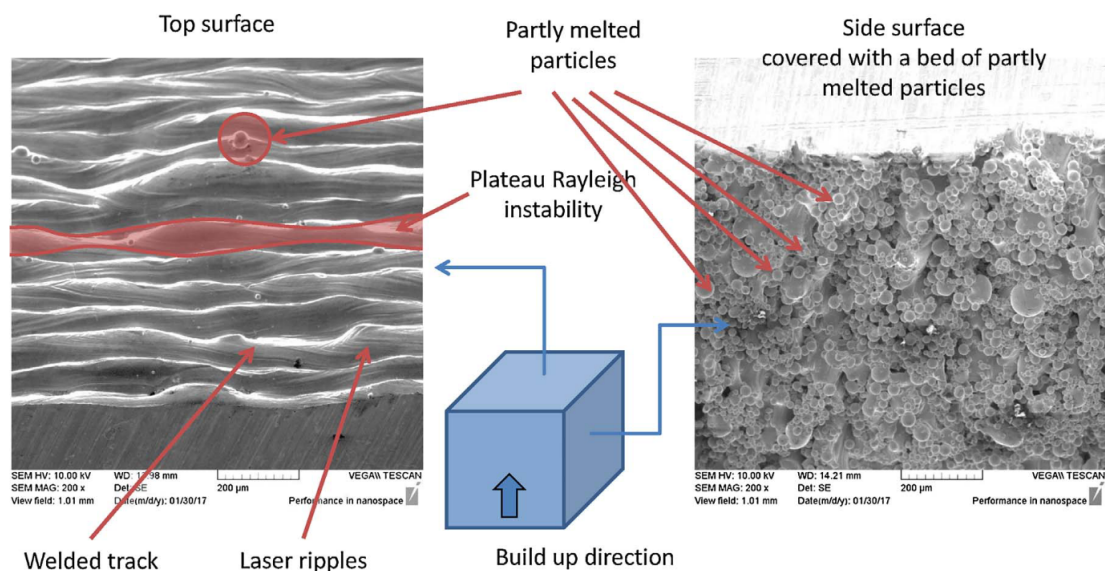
Topographie de surface typique d'une pièce fabriquée par procédé SLM [14]
